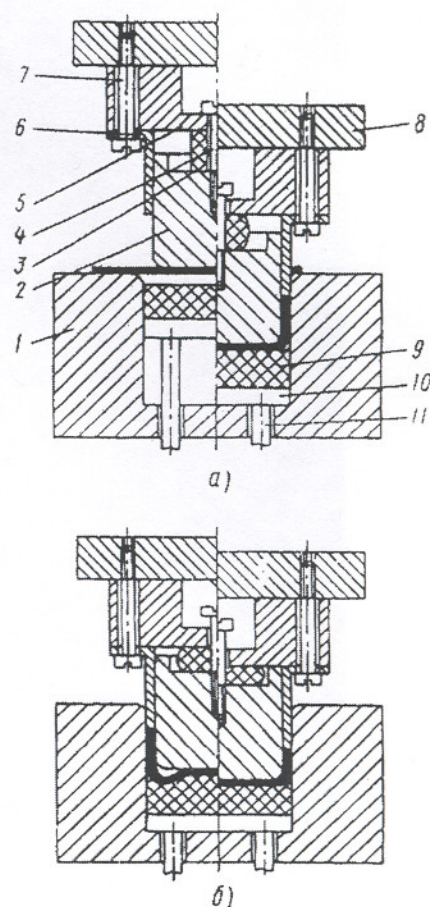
Устройство для вытяжки заготовки, обрезки припуска и увеличения толщины материала в зоне сопряжения дна со стенкой за один ход пресса: а, б – начальная и конечная стадии процесса
